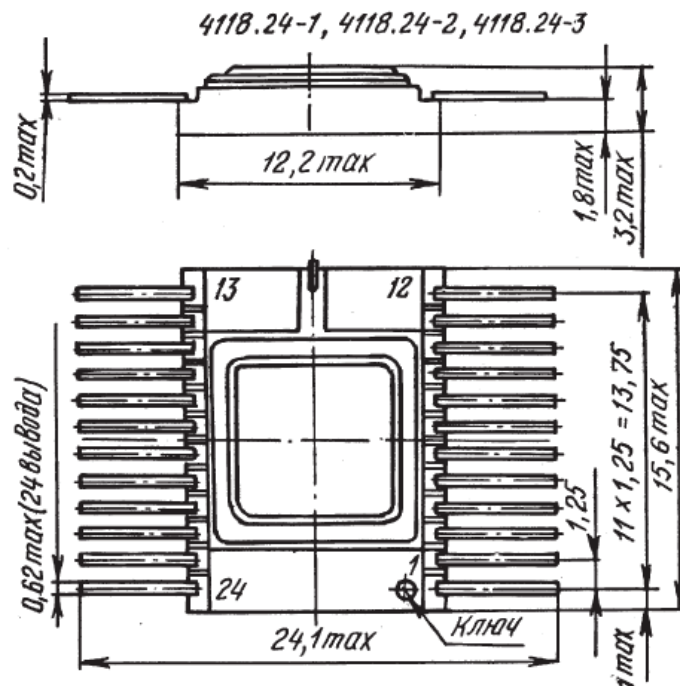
Габаритный чертеж корпуса 4118.24-1
